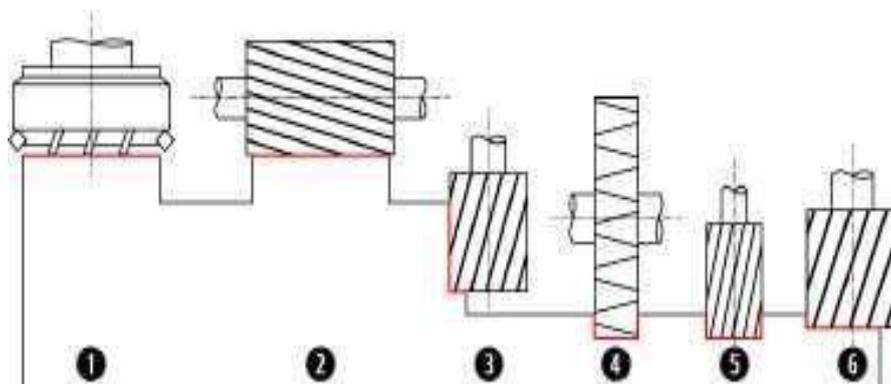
Les différentes opérations d'usinage pouvant être réalisées sur des machines-outils de type fraiseuse. [10]
